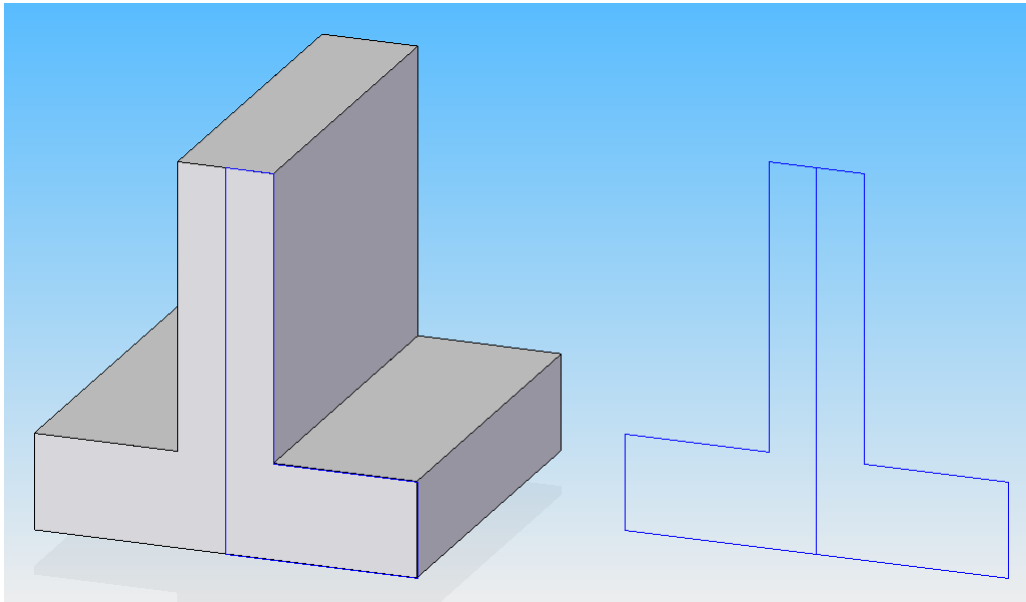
Funkce Zrcadlená kopie a výsledek
